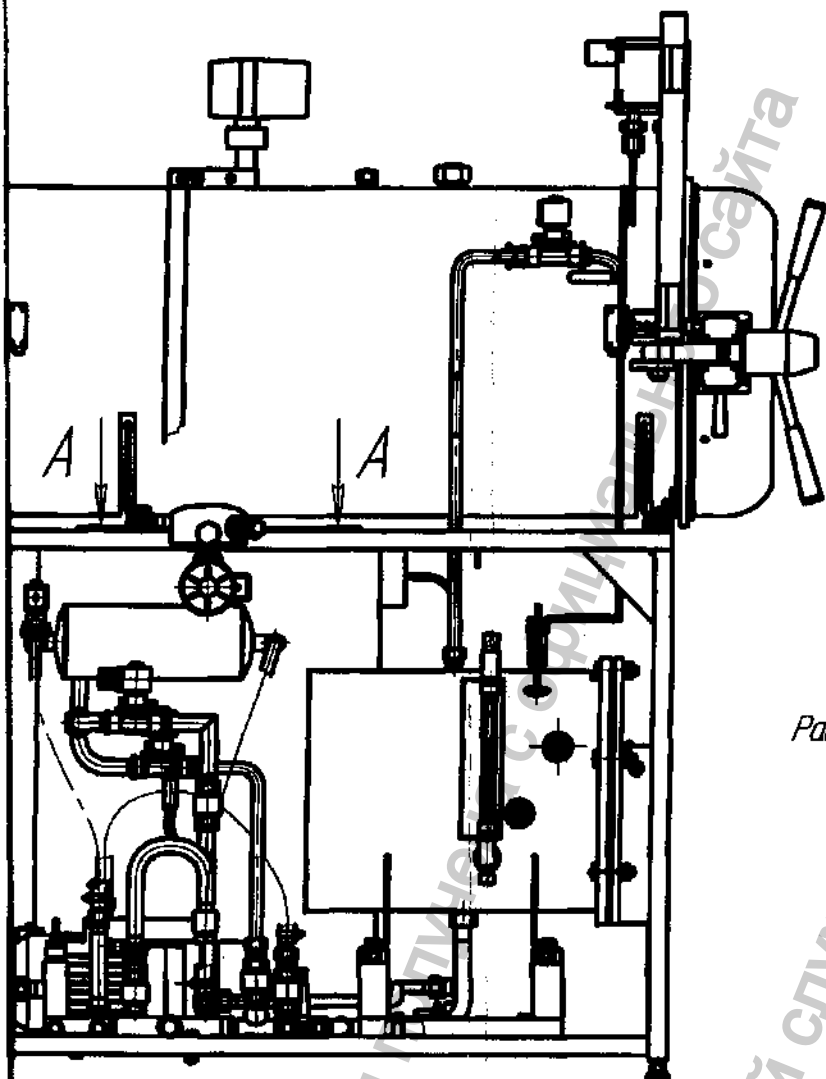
Стерилизатор паровой двухдверный ГКД-100-4-ТЗМО
